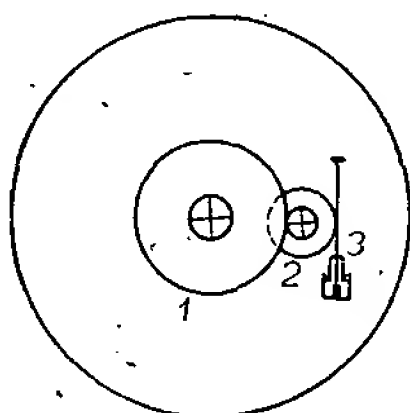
Číslo součástí se shodují s obr. 1; regulátor počtu otáček není zakreslen. 4 - panel magnetofonu
